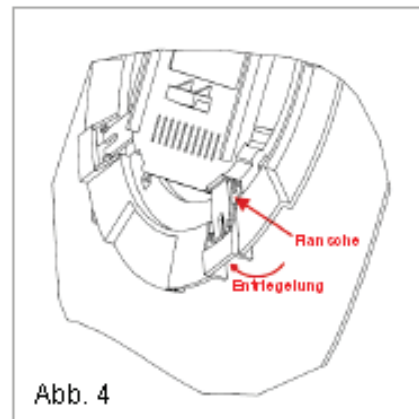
Die Flansche dienen zur Befestigung des Gerätes auf dem entsprechenden Panel. Es ist wichtig, dass die Flansche bei Befestigung der Anlage frei und entriegelt sind, sodass bei Andrücken des Ringes die Zähne der Zahnführung freigesetzt werden. Auf gleiche Weise müssen die Flansche bei Abnahme der Anzeige von dem Panel entriegelt, d.h., geöffnet werden, bevor mit dem Ausbau begonnen wird.
